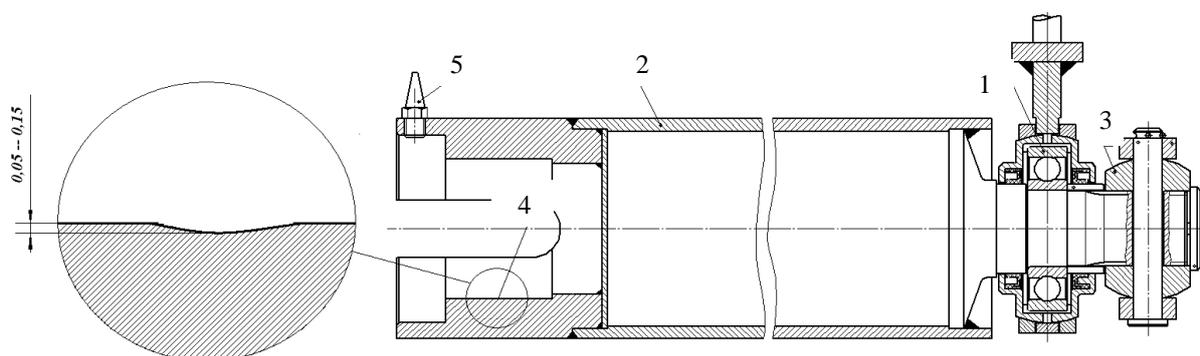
Расположение зоны износа на цилиндрической поверхности муфты:
